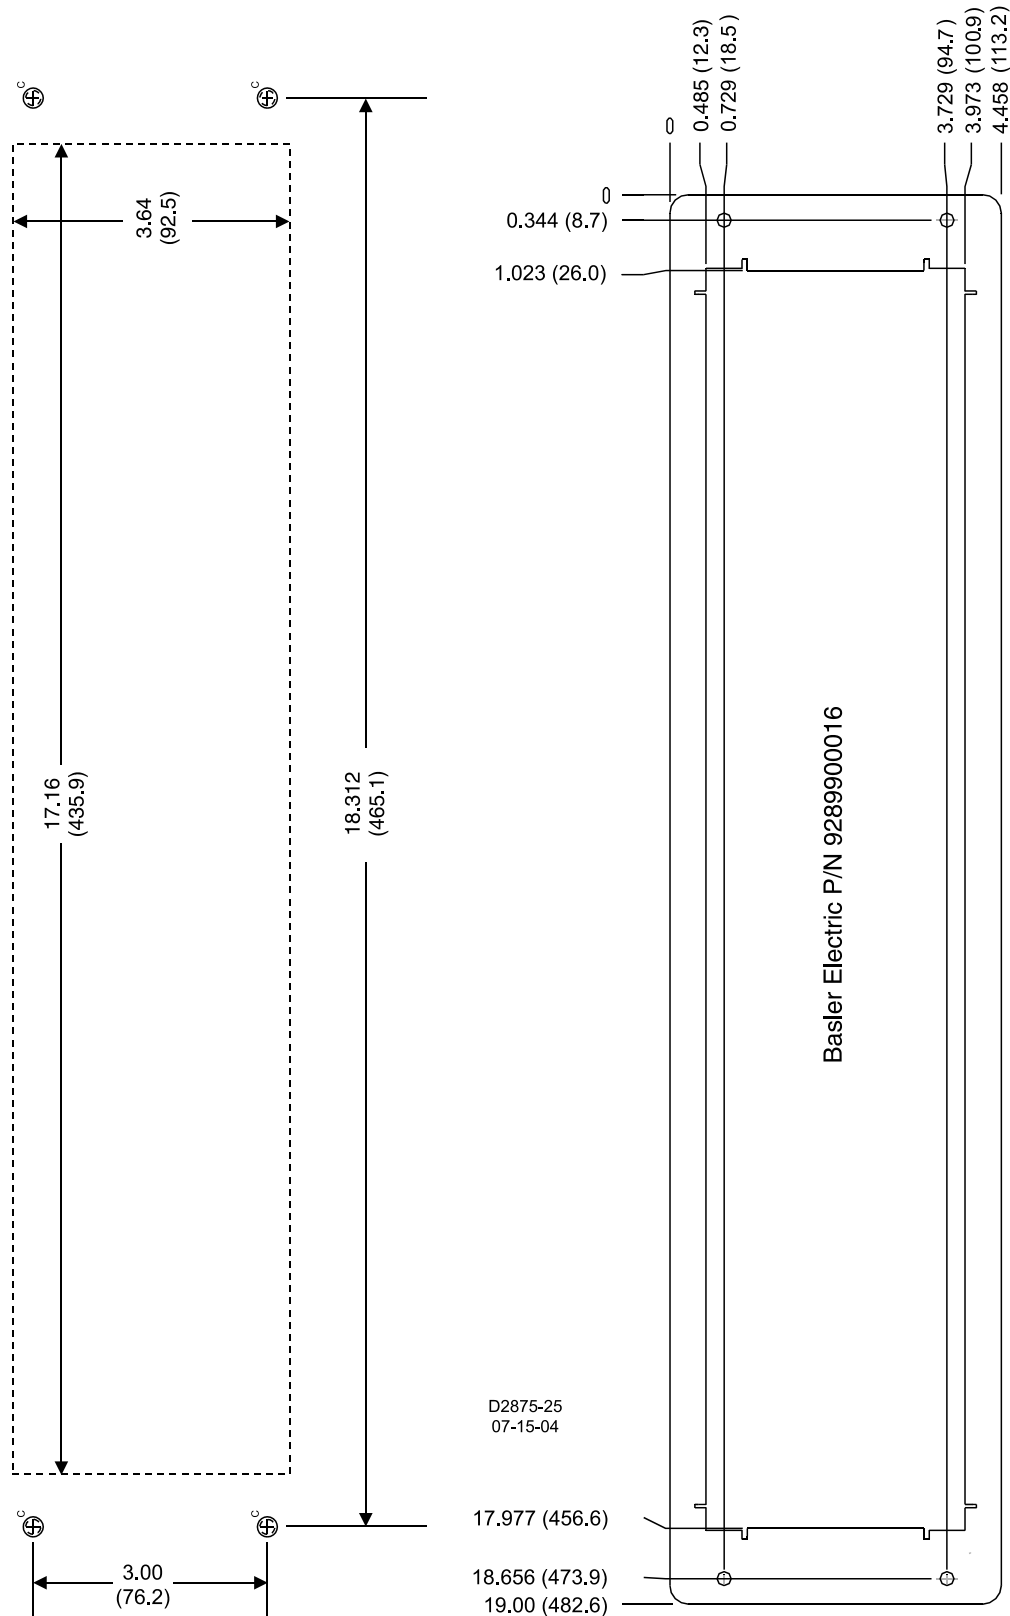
Dimensions de découpe et de socle de montage d'un BE1-11g H1 en queue-d'aronde
